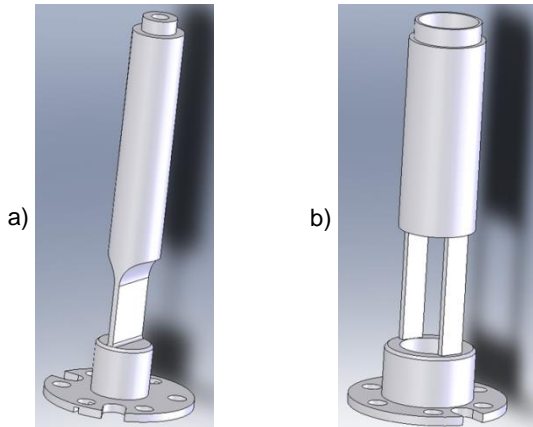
Konstrukcja sondy z czujnikiem bezdotykowym
